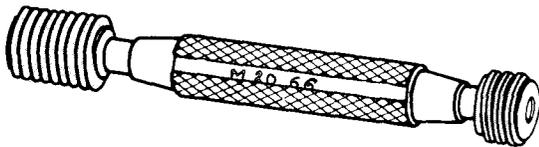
Calibre macho de tolerancia de rosca.
